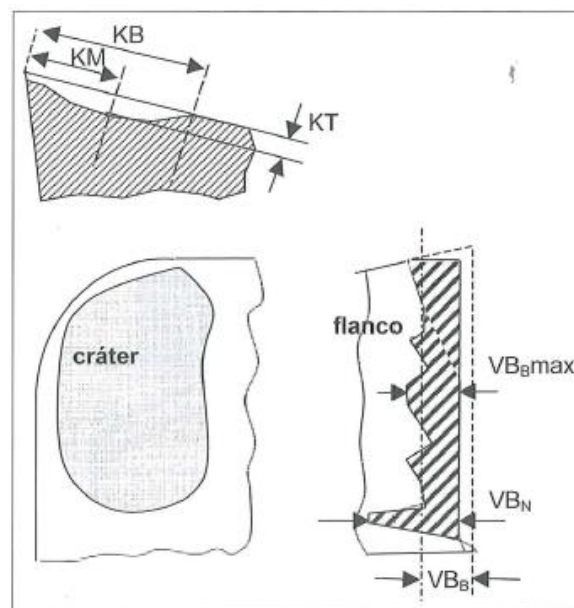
Zonas de desgaste presentadas en la herramienta[23].
